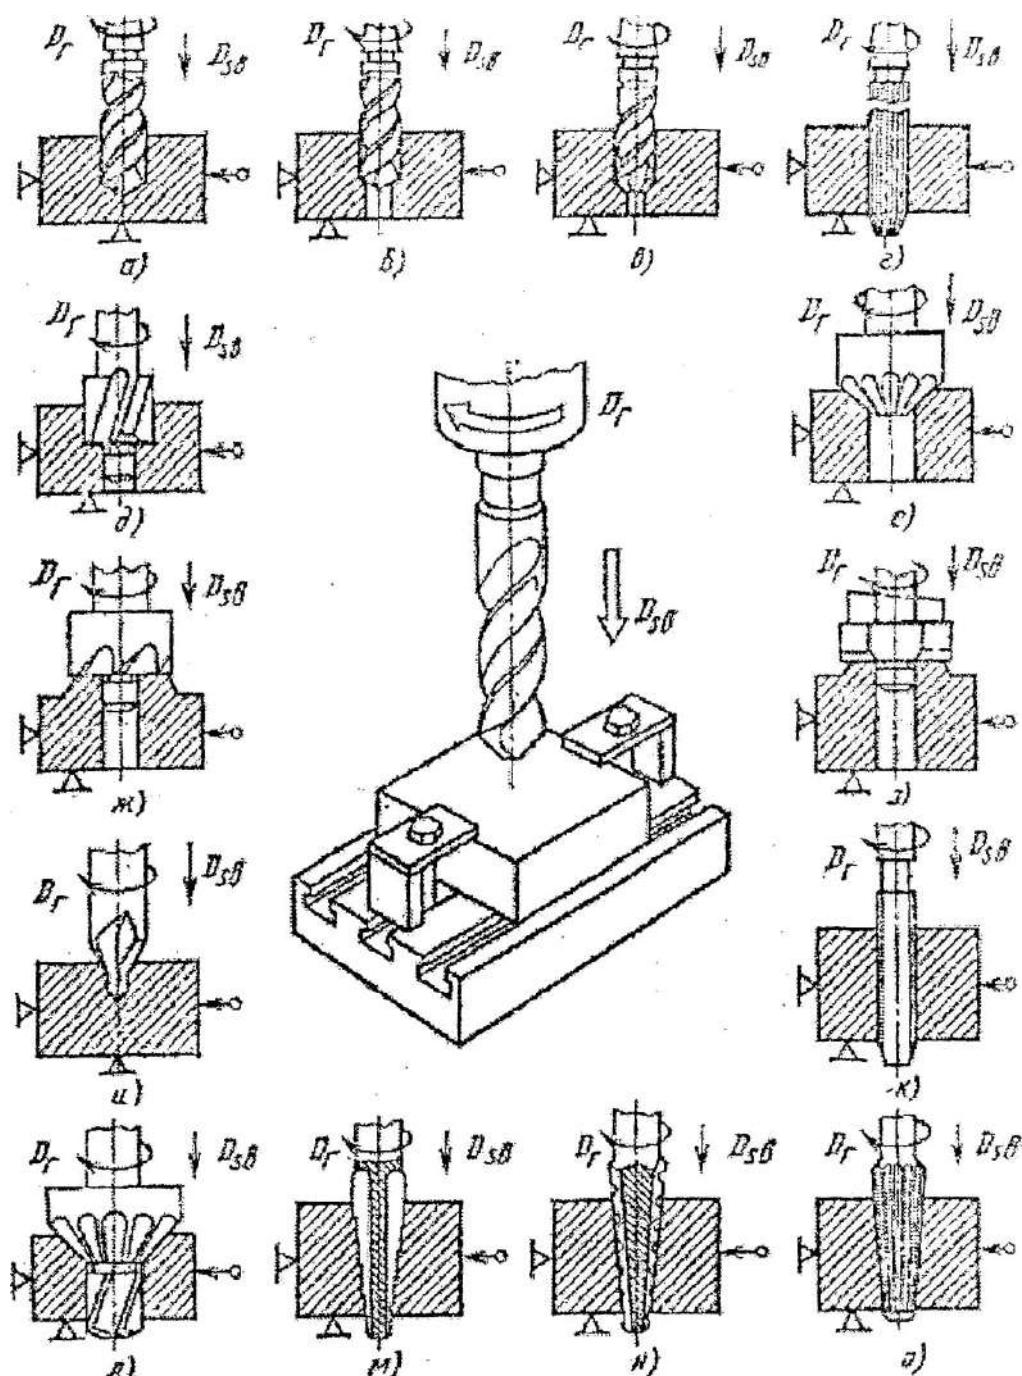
Схемы обработки заготовок на сверлильных станках
